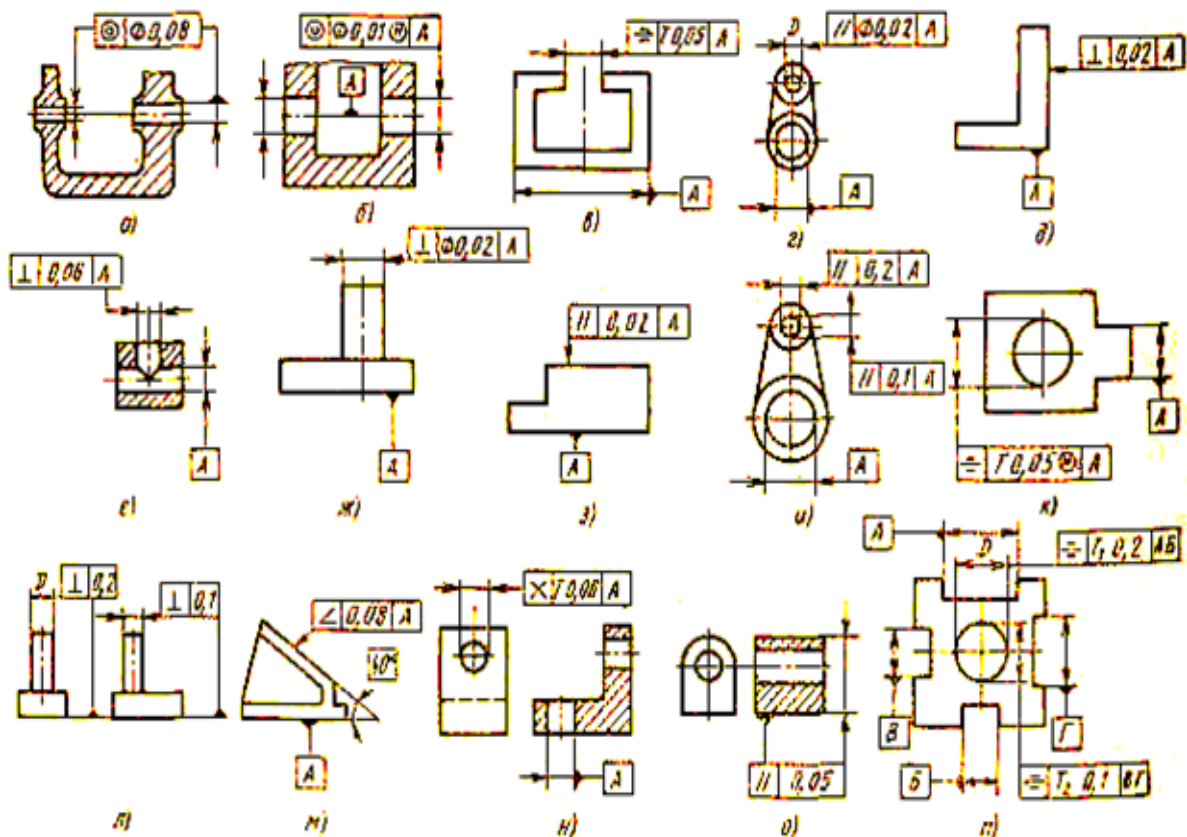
Условные обозначения допуска расположения поверхностей детали
